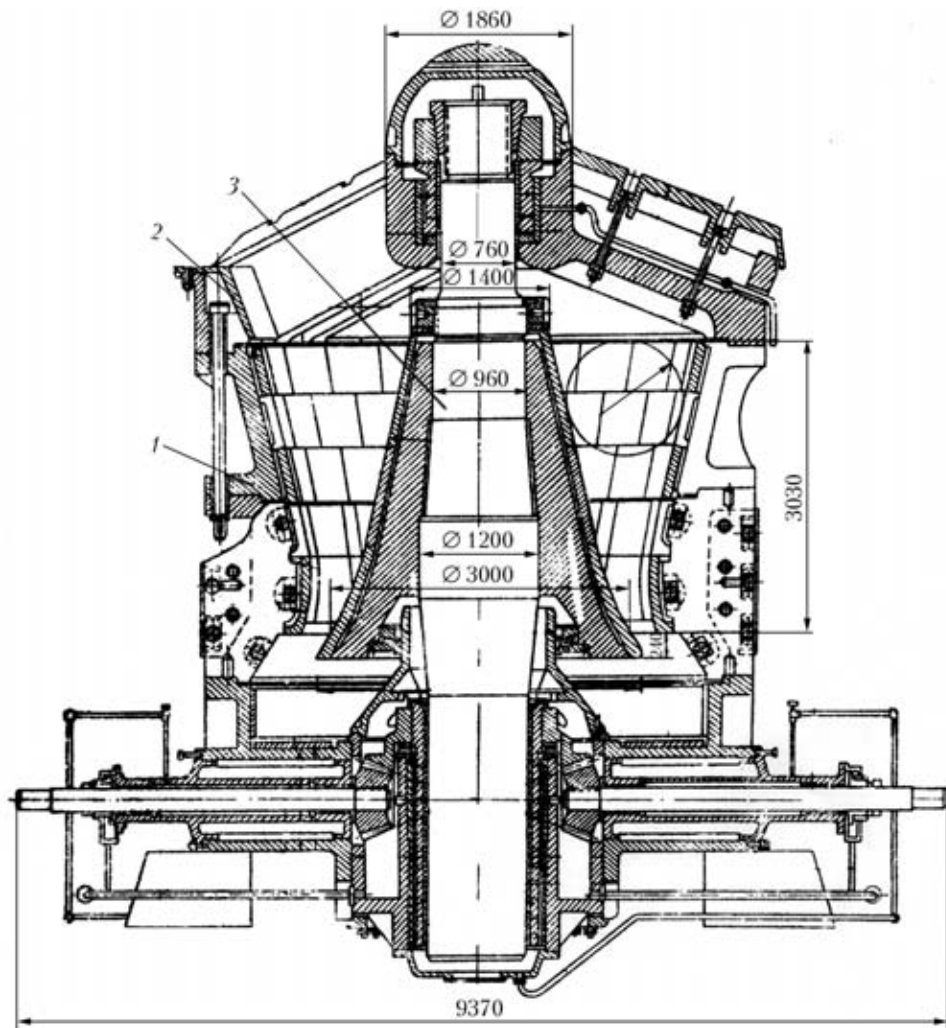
Схема конусной дробилки: 1 — станина; 2 — корпус кольца; 3 — вал
